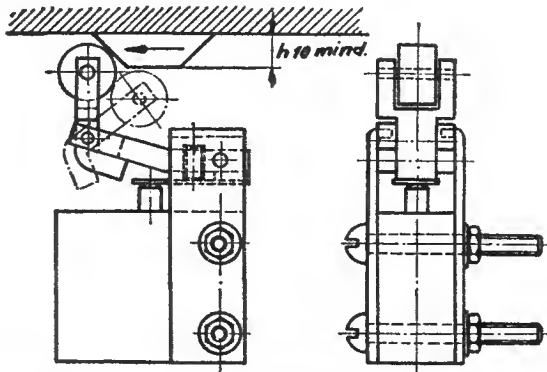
Nockenventil mit Rollenhebel und Leerrücklaufvorrichtung
